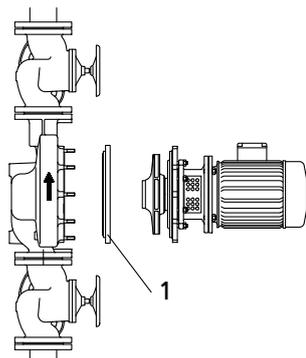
Montagem na horizontal com flange cego (1 = flange cego, acessório)
